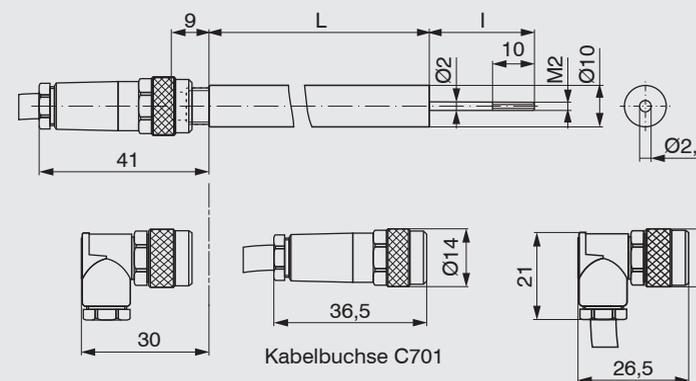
Wegsensor Typ - SA mit axialer Steckverbindung
